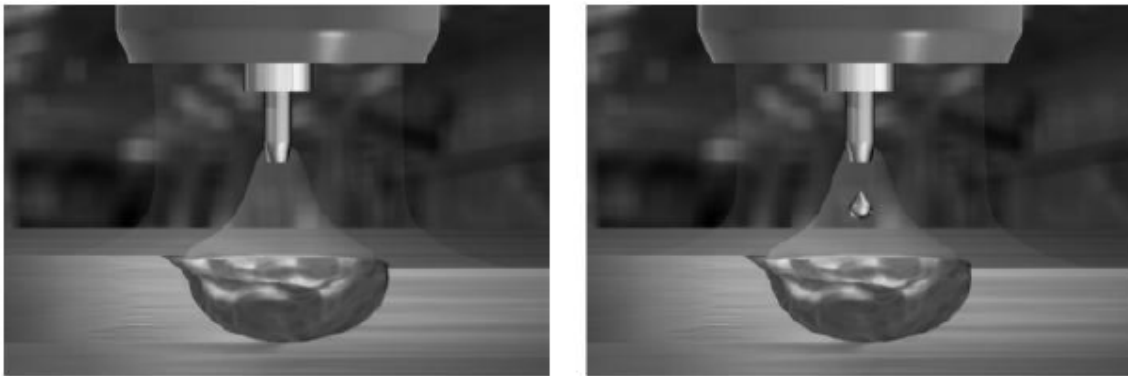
Soldadura MIG: curto-circuito e *spray* [40]
